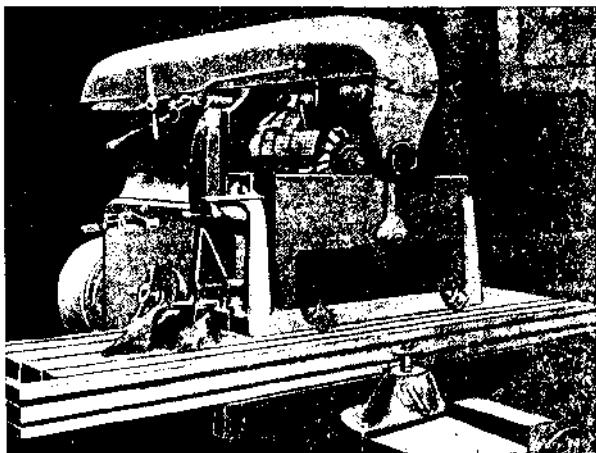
Фрезеровка гнезд подшипников на блоке Vauxhall.
